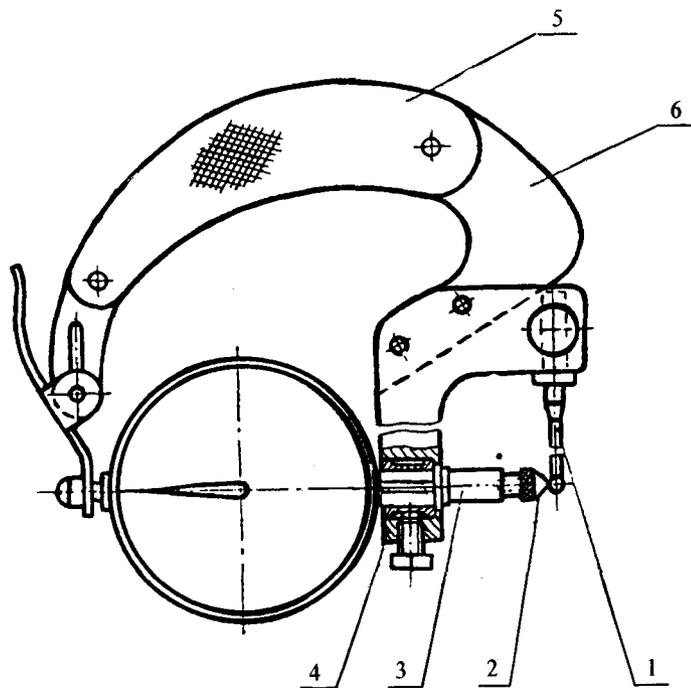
Приспособление для измерения толщин стенок распорных трубок:
